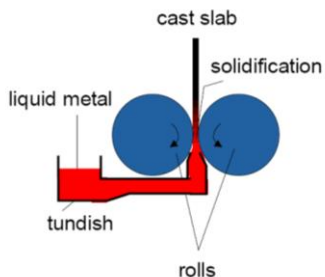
Representación esquemática de la máquina de colada de doble tambor diseñada por Hunter Engineering.
